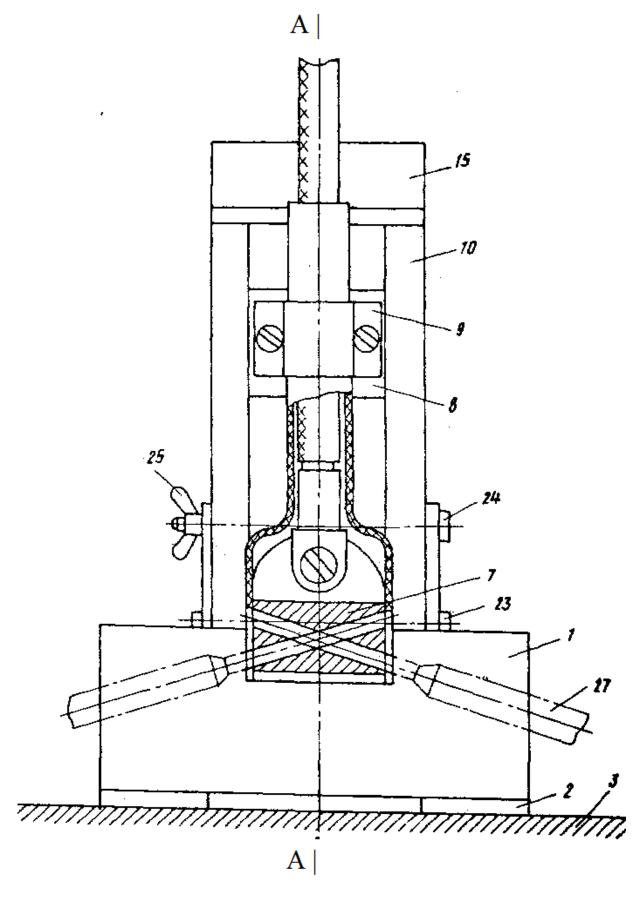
а - Устройство электрододержателя для сварки наклонным электродом
